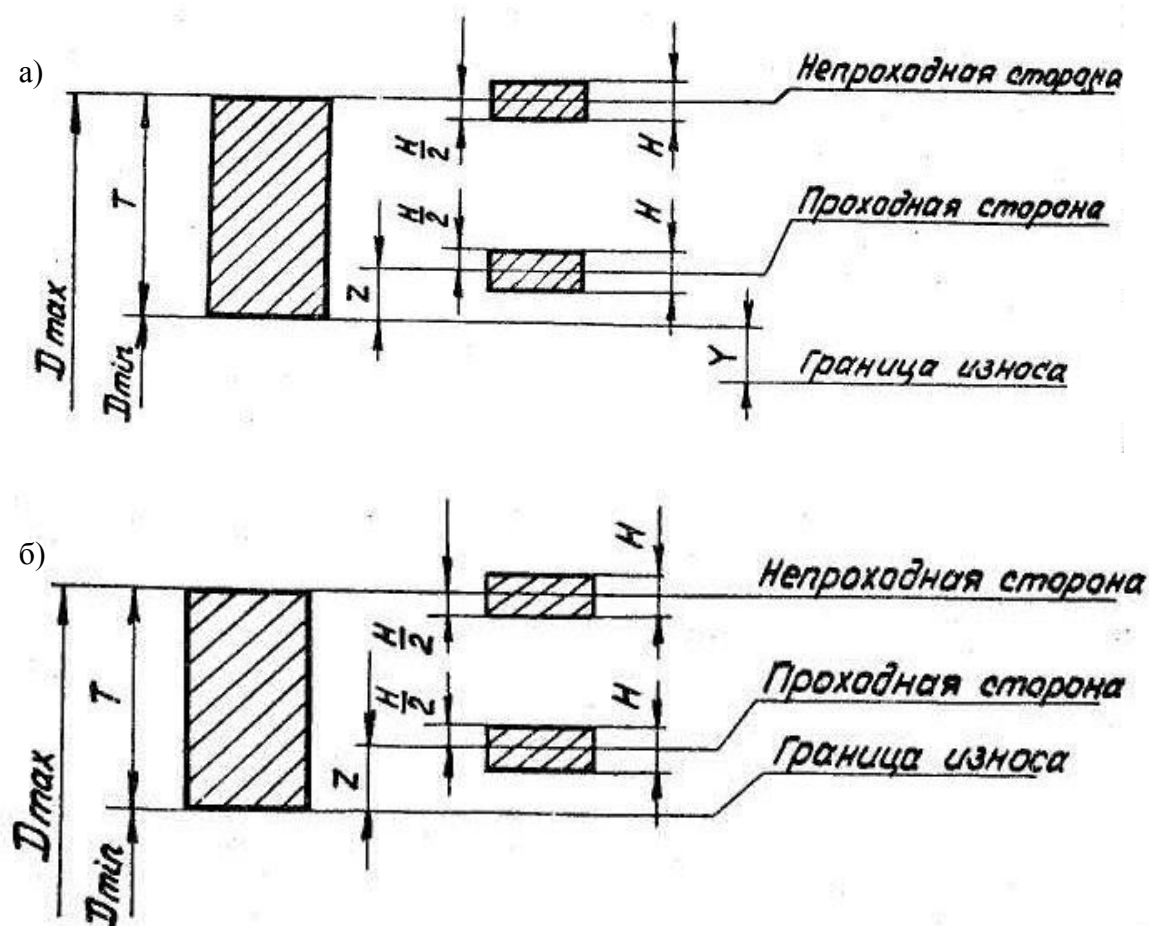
Схемы расположения полей допусков калибров-пробок для номинальных размеров до 180 мм
